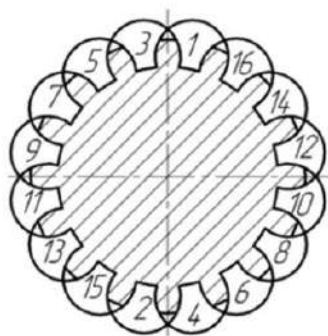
Порядок продольной наплавки цилиндрической детали способом уравнивающих валиков
